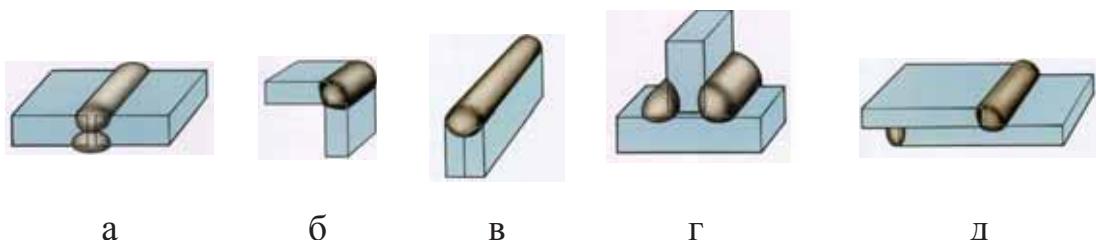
Типы сварных соединений: а –стыковое; б – угловое; в – торцевое; г – тавровое; д – нахлесточное
